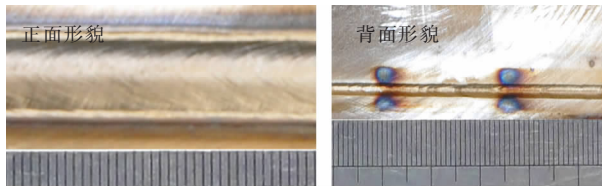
6 mm 厚不锈钢板 DP-TIG 焊接形貌
